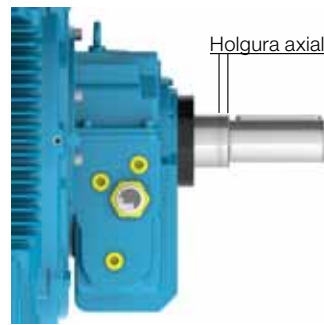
Holgura axial en motor equipado con cojinete de deslizamiento
